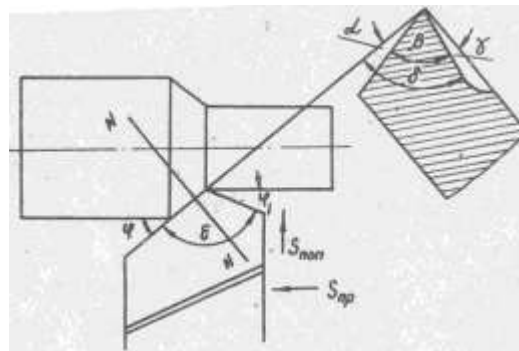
Геометрические параметры токарного проходного резца
